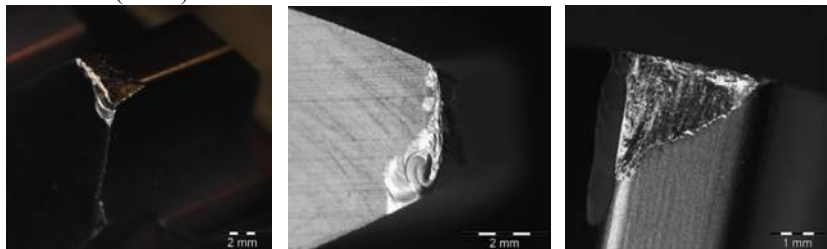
Разрушение режущих кромок инструмента для зуботочения
